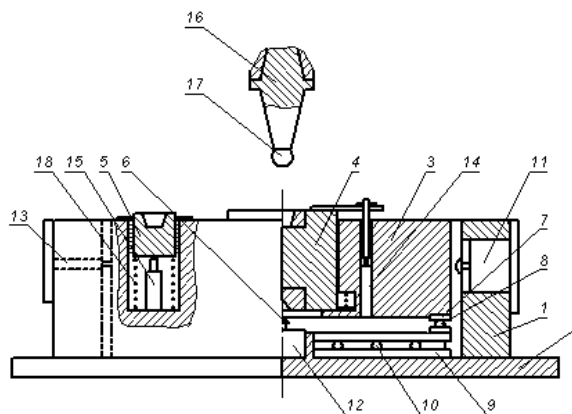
Устройство для испытания вертикально-фрезерного станка
